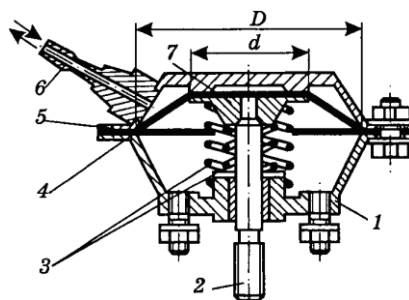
Мембранний пневмоциліндр: 1, 5 – частини корпусу; 2 – шток; 3 – пружини; 4 – діафрагма; 6 – патрубок; 7 – шайба
